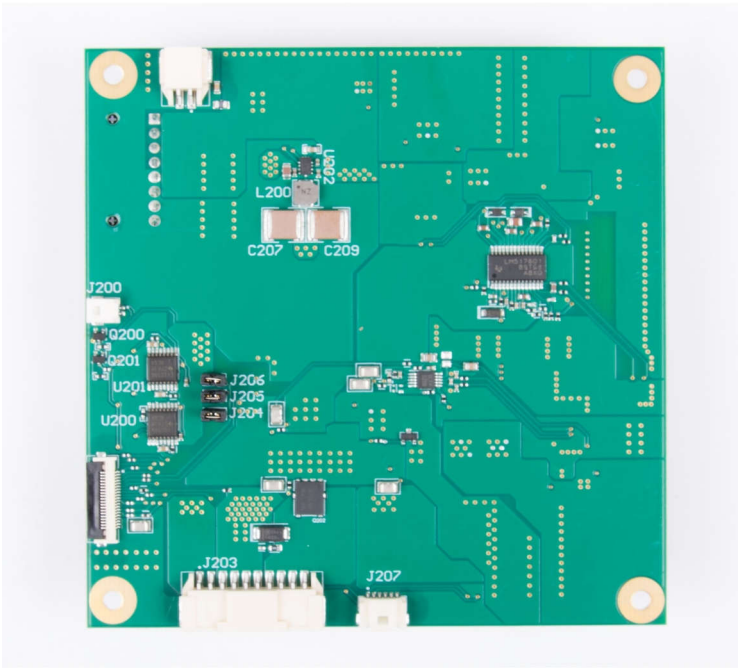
DLP5532PROJHBQ1EVM 照明驱动器 PCB (底部)
